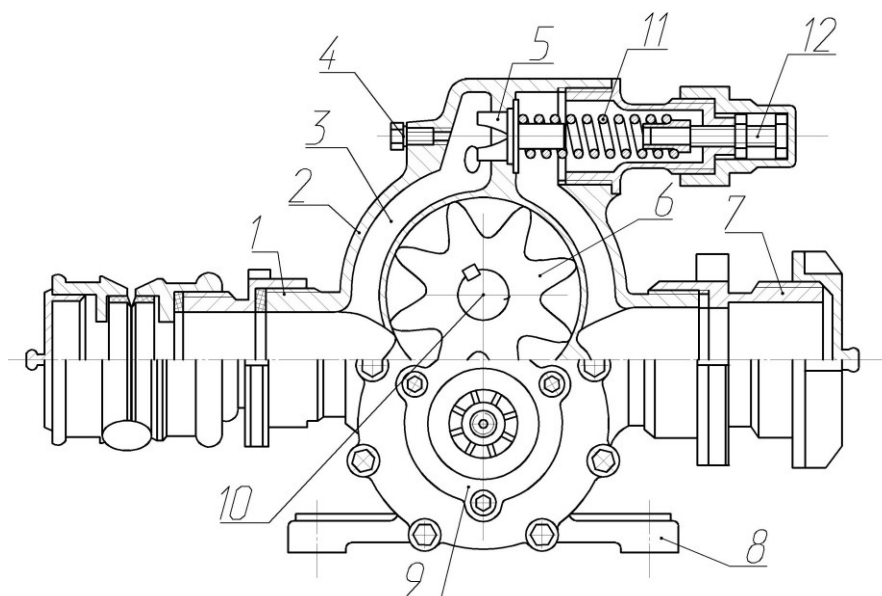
Навесной шестеренный насос НШН-600: 1-напорный патрубок; 2-корпус насоса; 3 - соединительный канал; 4 - заглушка; 5- предохранительный клапан; 6 - шестерня; 7 - всасывающий патрубок; 8 -
